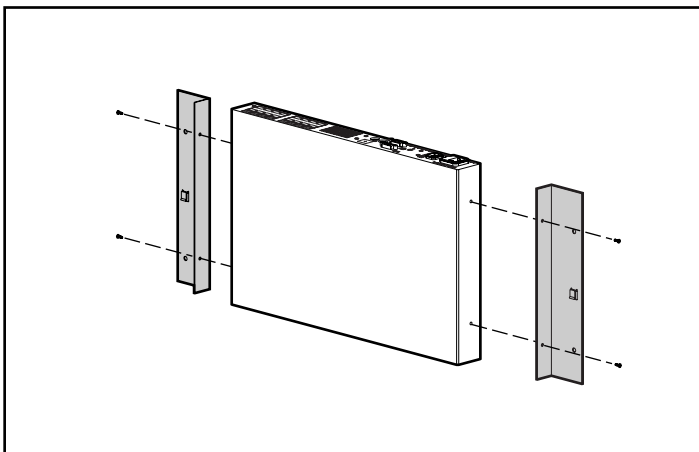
Fissaggio delle staffe per il montaggio laterale
